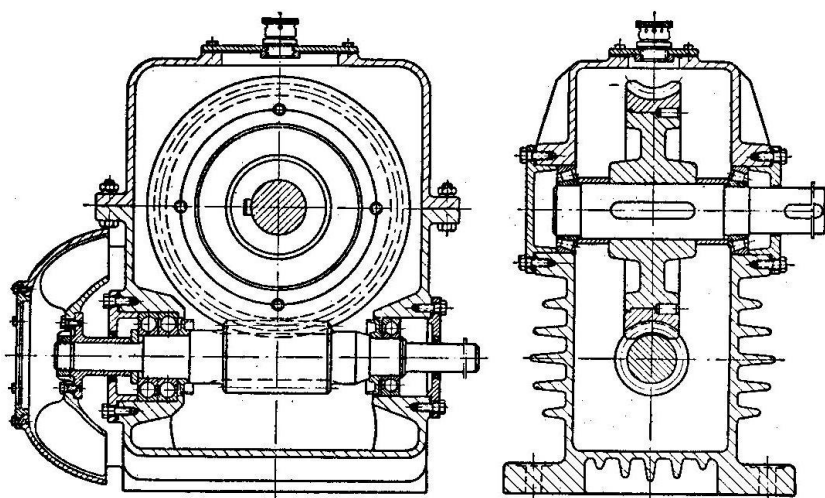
Червячный редуктор с горизонтальной осью червячного колеса
